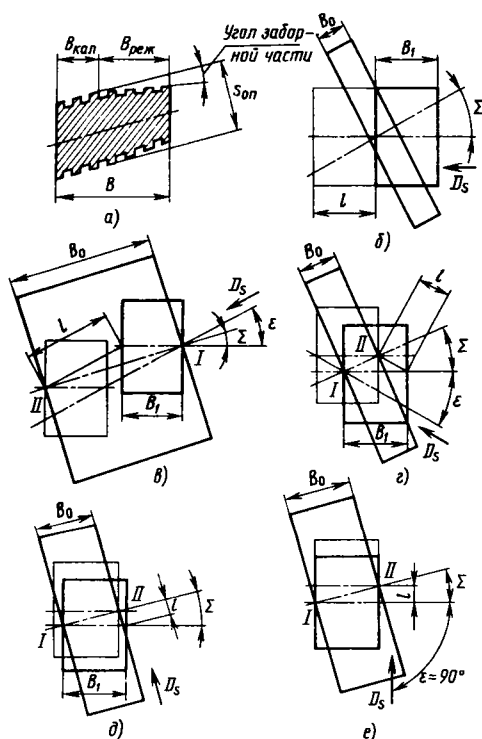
Шеверы однопроходные и с измененным направлением подачи
